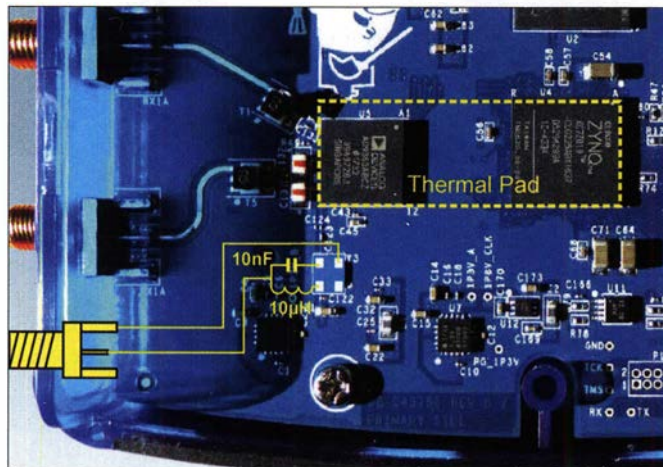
Platinausschnitt des Adalm Pluto; hier wurde der Original-TCXO bereits ausgelötet. Die Verdrahtung zur externen Einspeisung des Referenztakts ist angedeutet, ebenso die Lage des Thermal-Pads.
